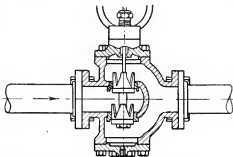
16. Регулирующий клапан типа ВО с треугольными проходами.
